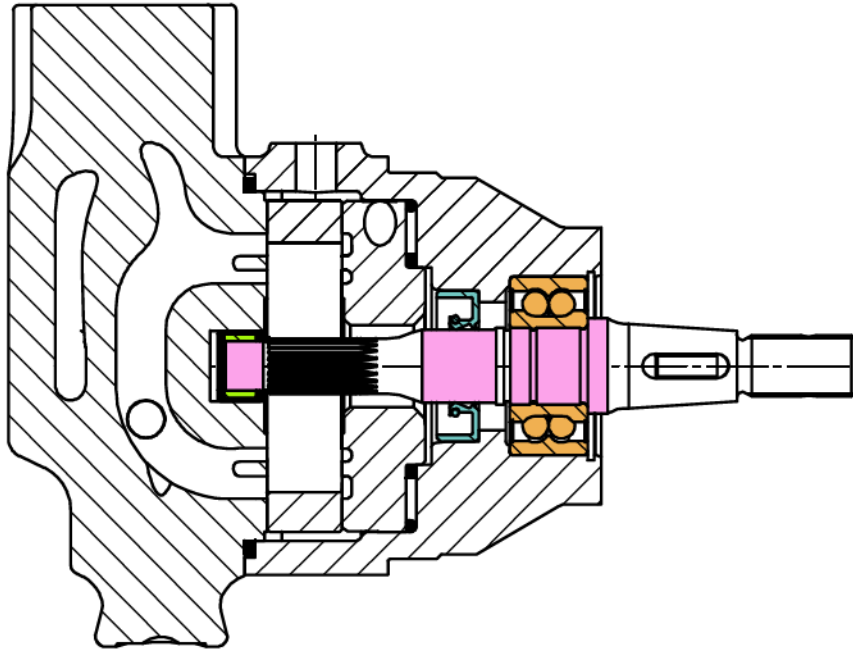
vue en coupe du moteur sans rotor et sans palettes
